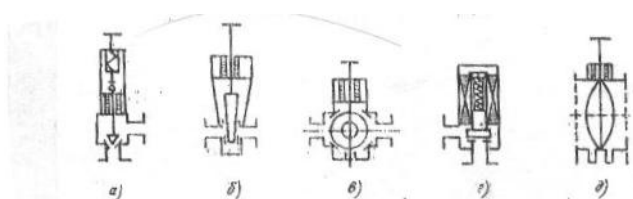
Конструктивные схемы запорной ГПТА: а – запорный клапан; б – задвижка; в – шаровой кран; г – электромагнитный клапан; д – дисковый затвор.
